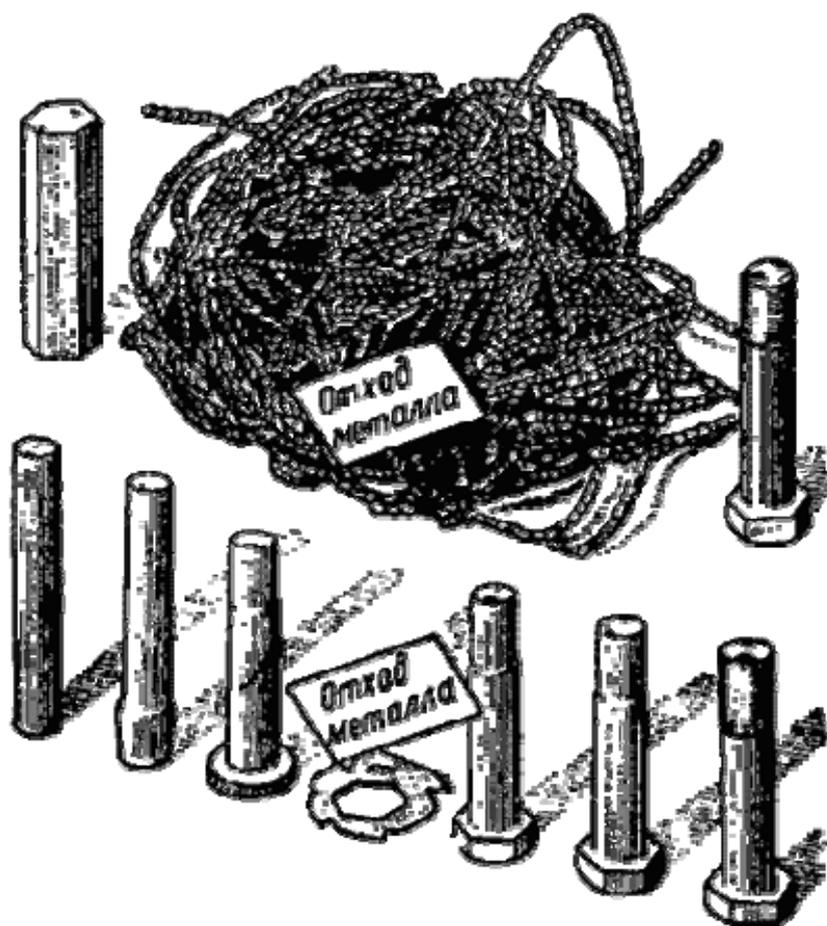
Отходы металла при изготовлении болта на токарном автомате (а) и методом холодной высадки с последующей накаткой резьбы (б)
